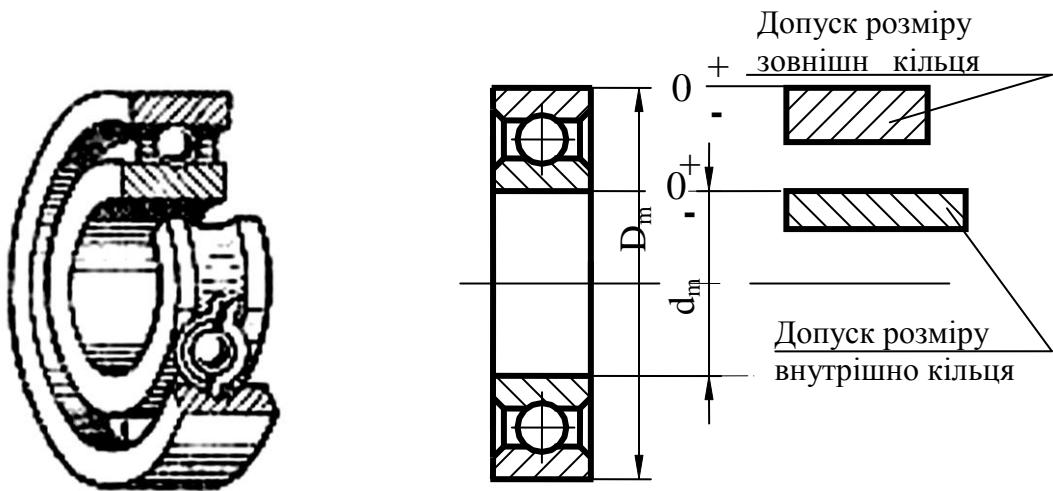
Підшипник кочення (а) і схеми розташування полів допусків на виготовлення його кілець (б)
